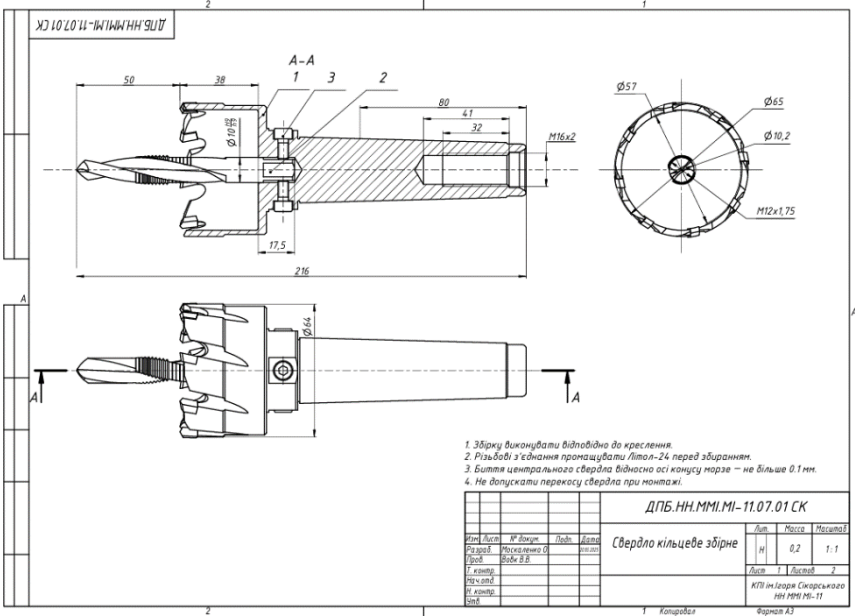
Кільцеве свердло складальний кресленник
